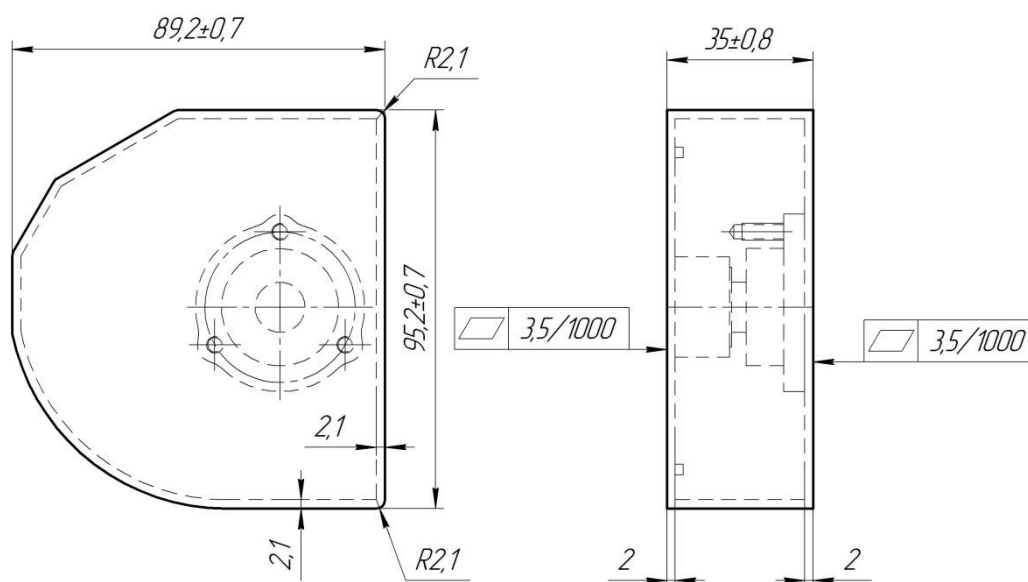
Заготовка, полученная на гидроабразивном станке.
